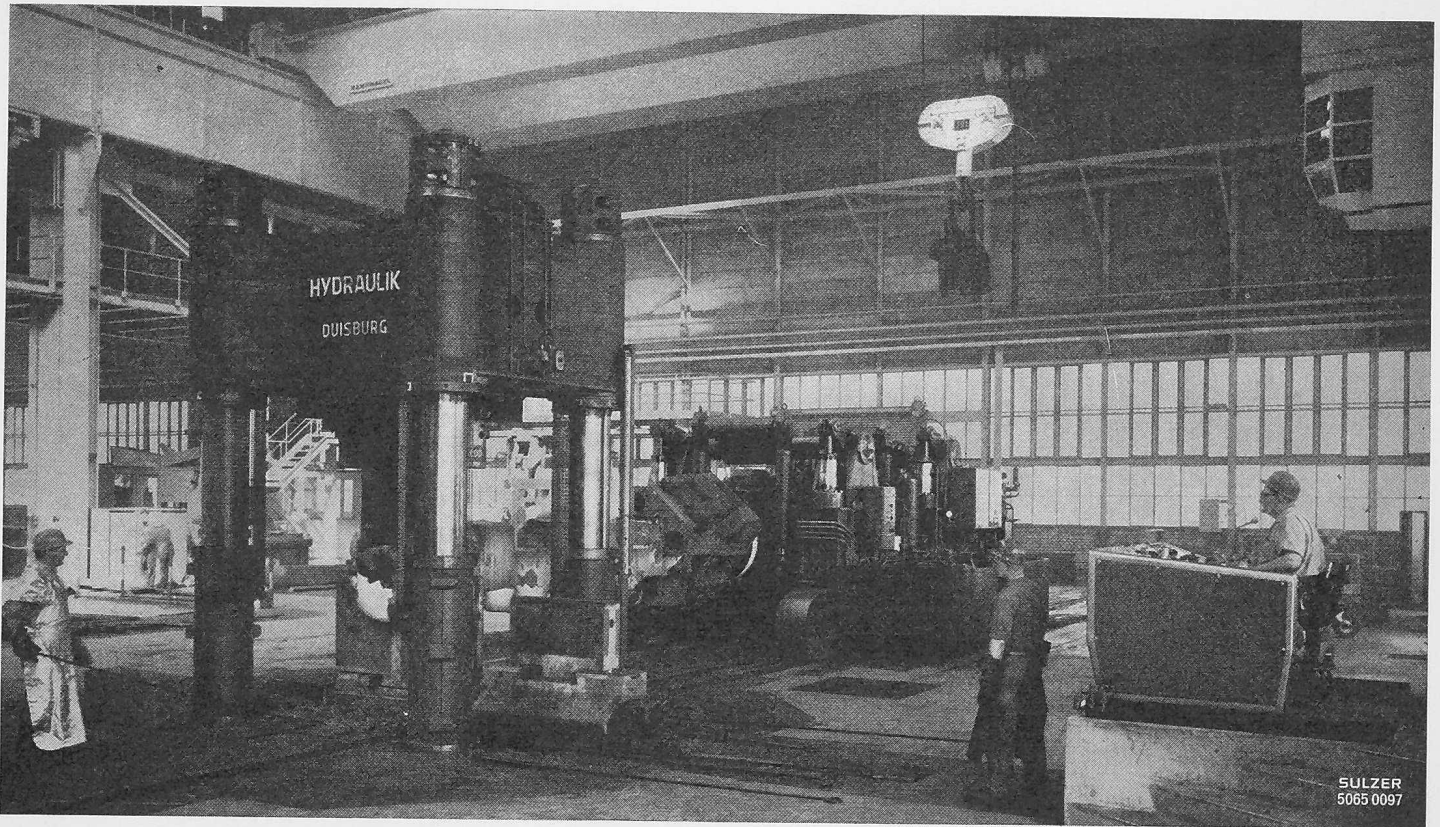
Ansicht der 2000-t-Schmiedepresse (links) mit Bedienungspult (rechts) und Schmiedemanipulator (Mitte, hinten)
